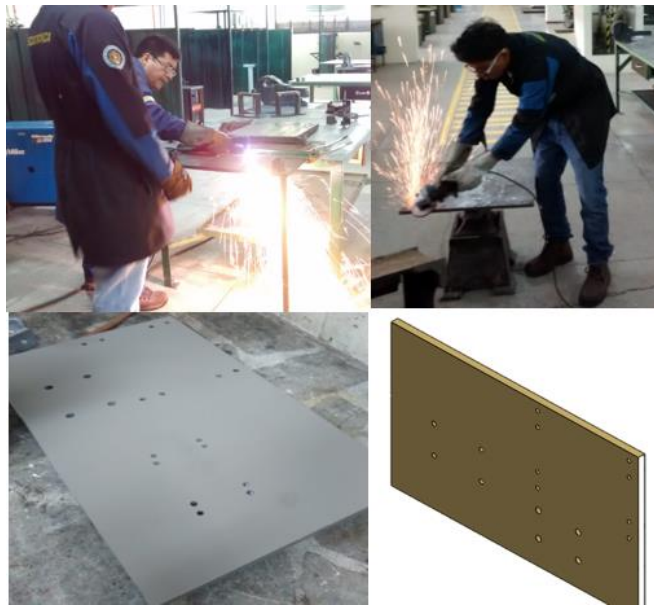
Mecanización de la base (Corte – Taladrado - Esmerilado)
